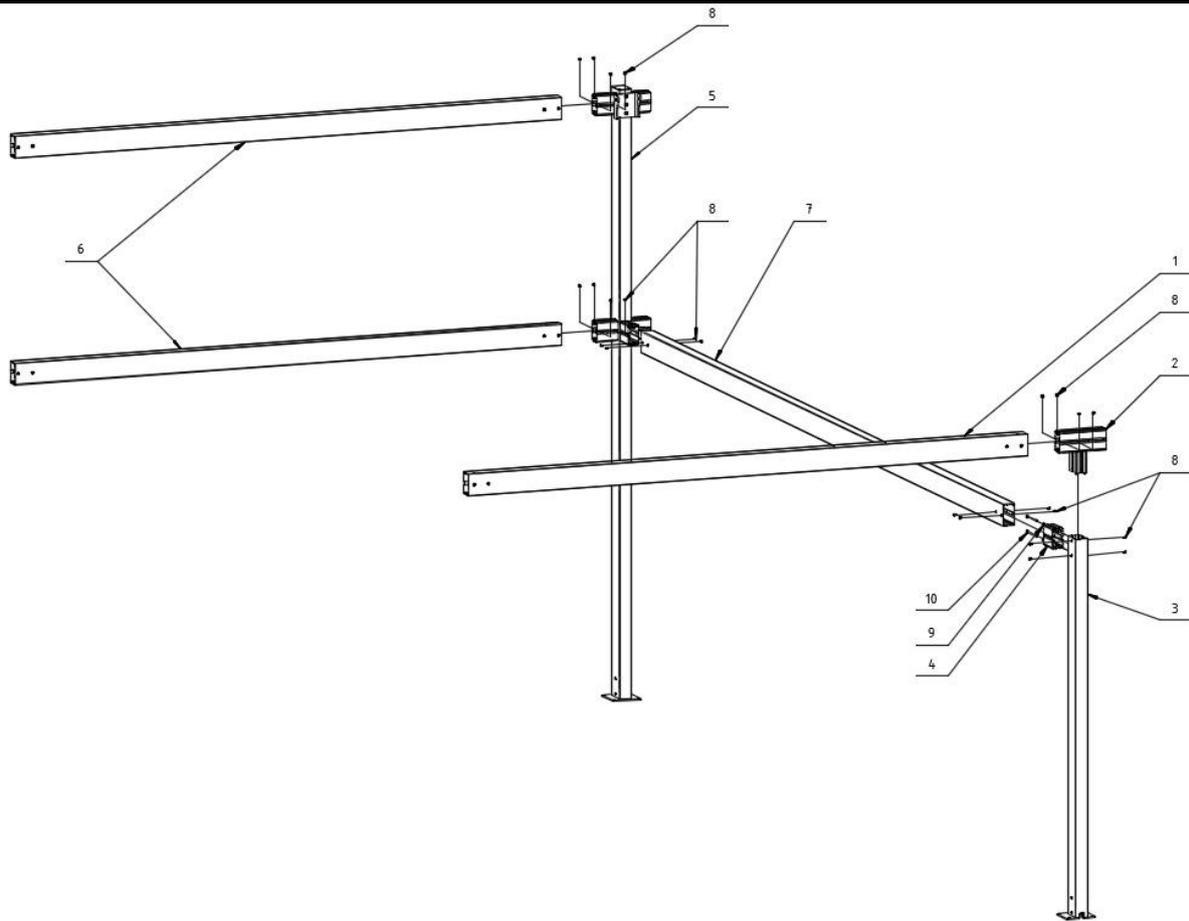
Méthode d'installation du module suivant (intermédiaire/fermeture) : 1 - Poutre avant (gauche/droite) ou Poutre avant (intermédiaire), 2 Connecteur "Connexion module", 3 - Poteau bas, 4 - Connecteur linéaire, 5 - Poteau haut (gauche/droite) ou Poteau haut (intermédiaire), 6 Poutre arrière, 7 Poutre latérale, 8 - Vis M8x16, 9 Rondelle  $\varnothing 8,4$ , 10 - Vis M8x180. Méthode d'installation du module suivant (intermédiaire/fermeture) : 1 - Poutre avant (gauche / droite) ou Poutre avant (intermédiaire), 2 Connecteur "Connexion modulaire", 3 - Montant bas, 4 - Connecteur linéaire, 5 - Montant haut (gauche / droite) ou Montant haut (intermédiaire), 6 Poutre arrière, 7 Poutre latérale, 8 - Vis M8x16, 9 Rondelle  $\varnothing 8,4$ , 10 - Vis M8x180.
